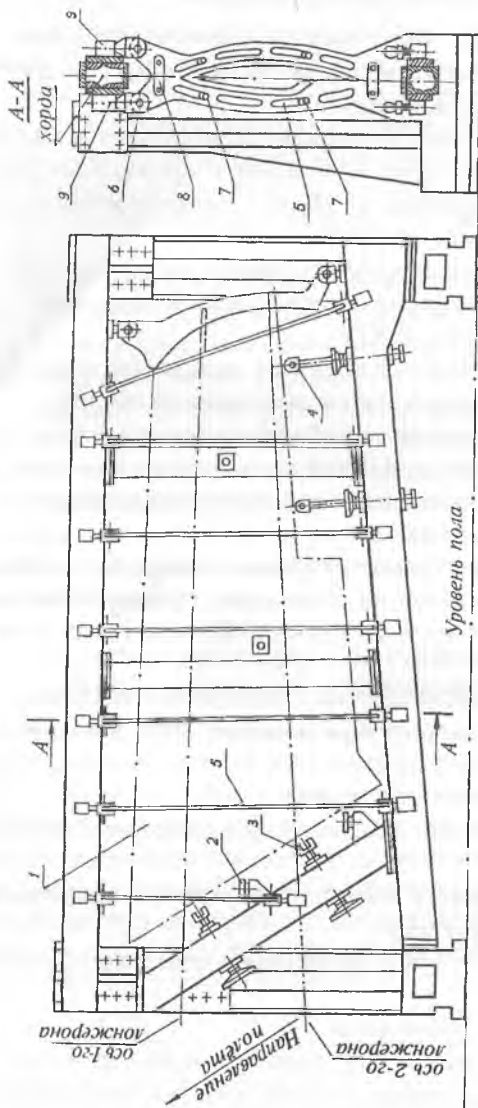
Сборочное приспособление с установленным в нем монтажным эгалом: 1 — монтажный эгалон; 2 — репер; 3 — стыковой узел приспособления; 4 — узел разъема на приспособлении; 5 — рубильник; 6 — вилка; 7 — фиксатор; 8 — накладка; 9 — стакан
